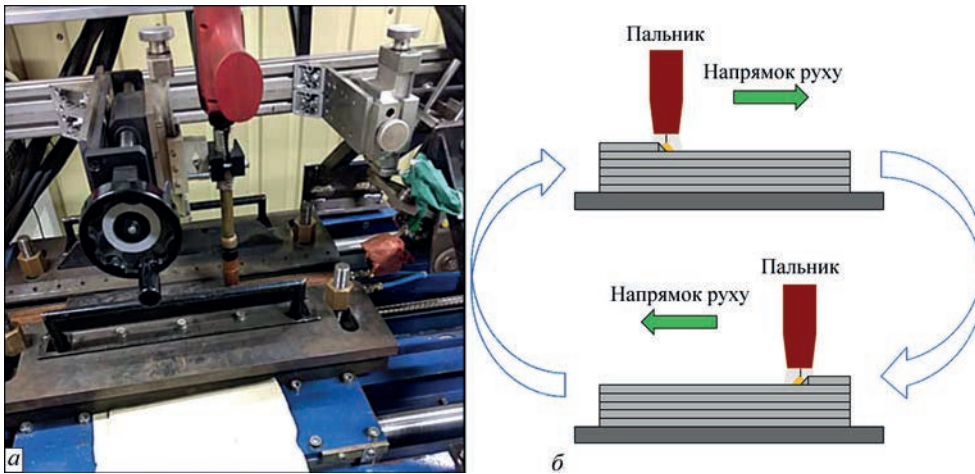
Обладнання та методика наплавлення: а – стэнд для наплавлення прямолінійних швів; б – напрямок руху пальника при пошаровому наплавленні
